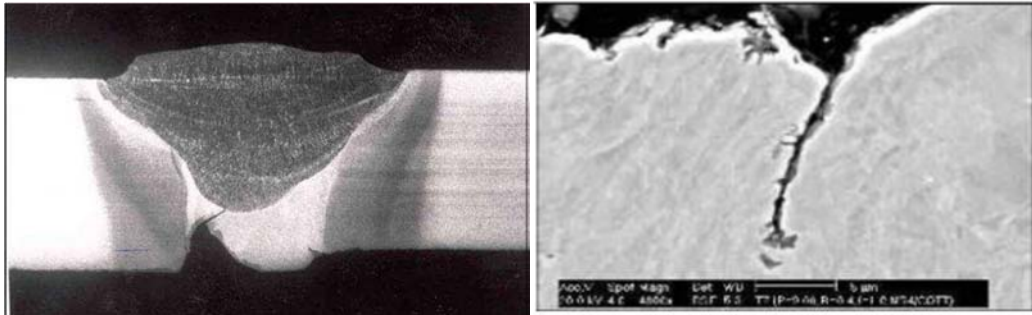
Fissure dans des joints soudés [10]
